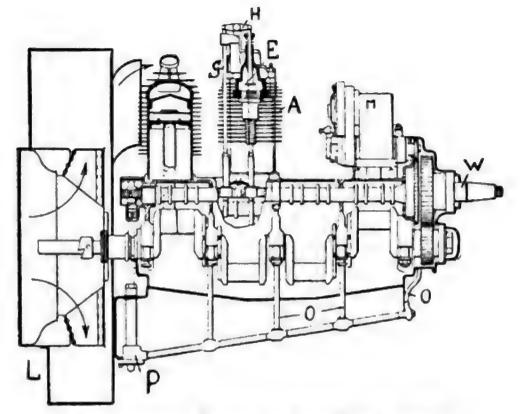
Luftgekühlter Flugmotor von Renault Frères. Längsschnitt.
